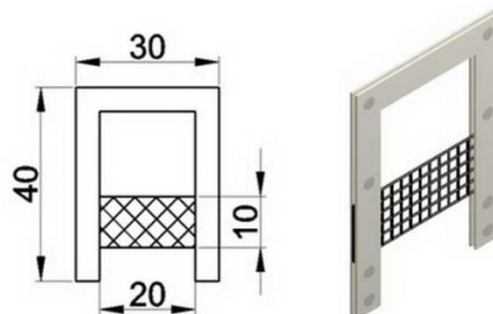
Образец, закрепленный в рамку из нержавеющей стали 12X18H10T
